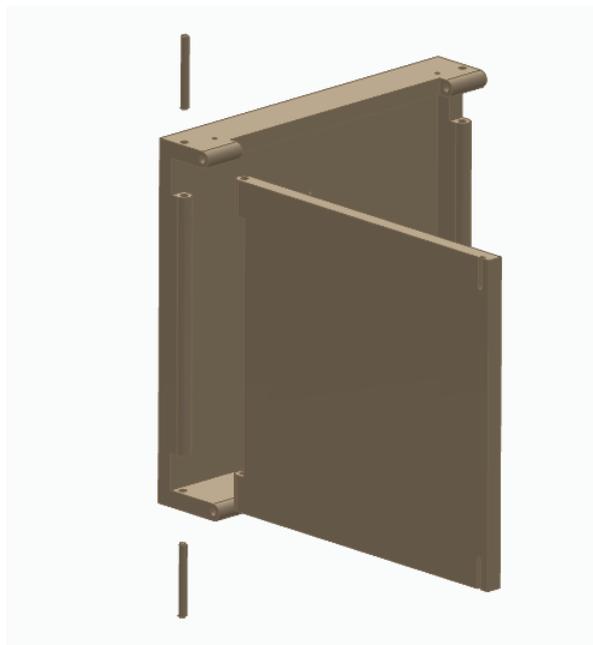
Posicionamiento de tablero izquierdo e inserción de ejes
